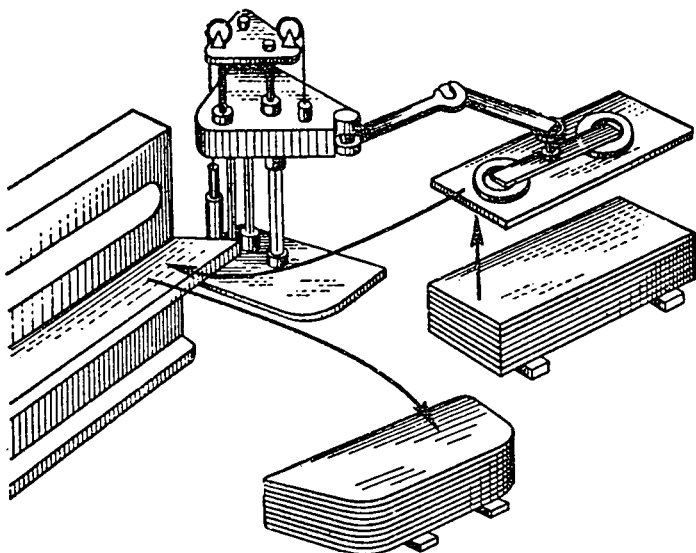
Пневматический манипулятор конструкции ЭНИКМаш
